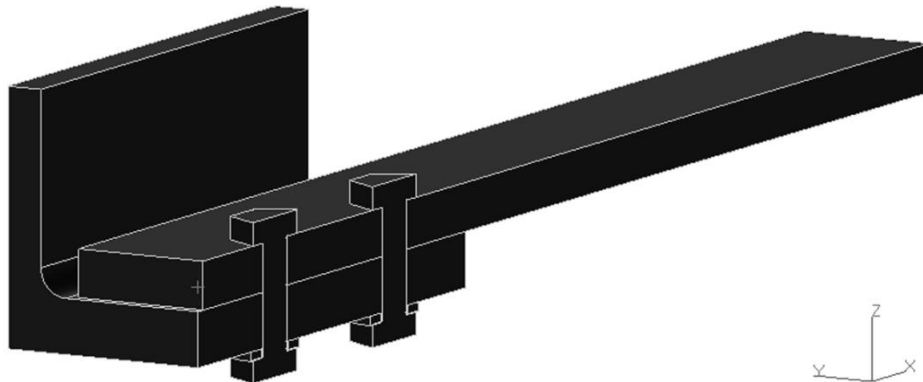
Розрахункова, у чверть зразка, геометрична модель зразка однозрізного болтового з'єднання деталей із ПКМ
